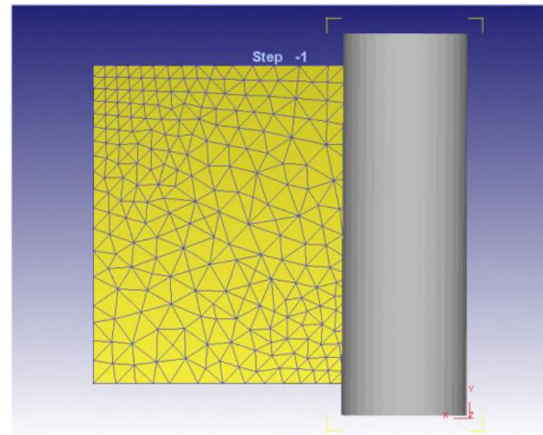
Позиціонування інструменту відносно заготовки (вид зверху)
